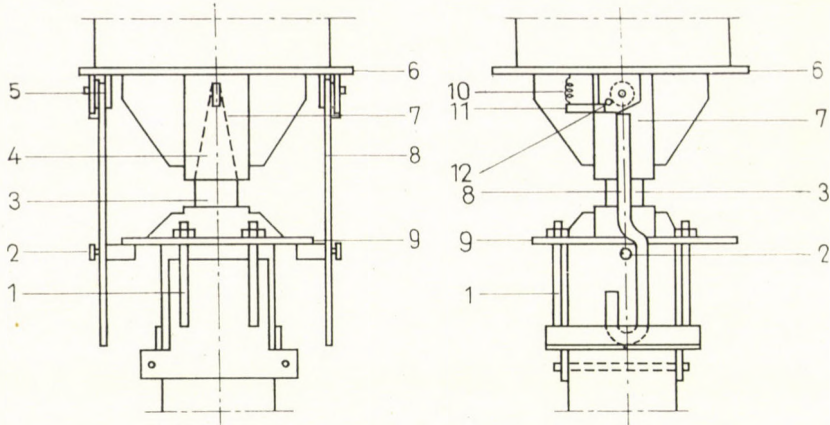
Vorrichtung zum gleichzeitigen Heben des Pfahles und des Schlagrüttlers. 1 — Schrauben; 2 — Gleitmutter; 3 — Bolzen des Kegels; 4 — Kegel; 5 — Befestigungsvorrichtung; 6 — Grundplatte; 7 — Haube; 8 — Haken; 9 — Platte des Kegels; 10 — Feder; 11 — Hebel; 12 — Sperrvorrichtung
